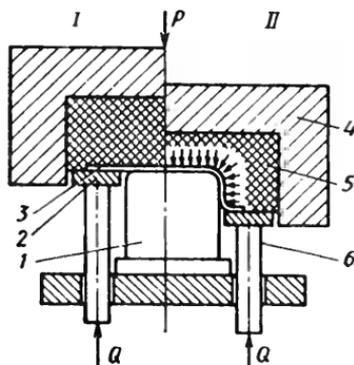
Штамповка деталей с применением резины: I – исходное положение; II – положение при вытяжке; 1 – жесткий пуансон (формообразующая деталь); 2 – прижимная плита; 3 – заготовка; 4 – контейнер для размещения резины; 5 – резиновая матрица; 6 – стержень прижима
